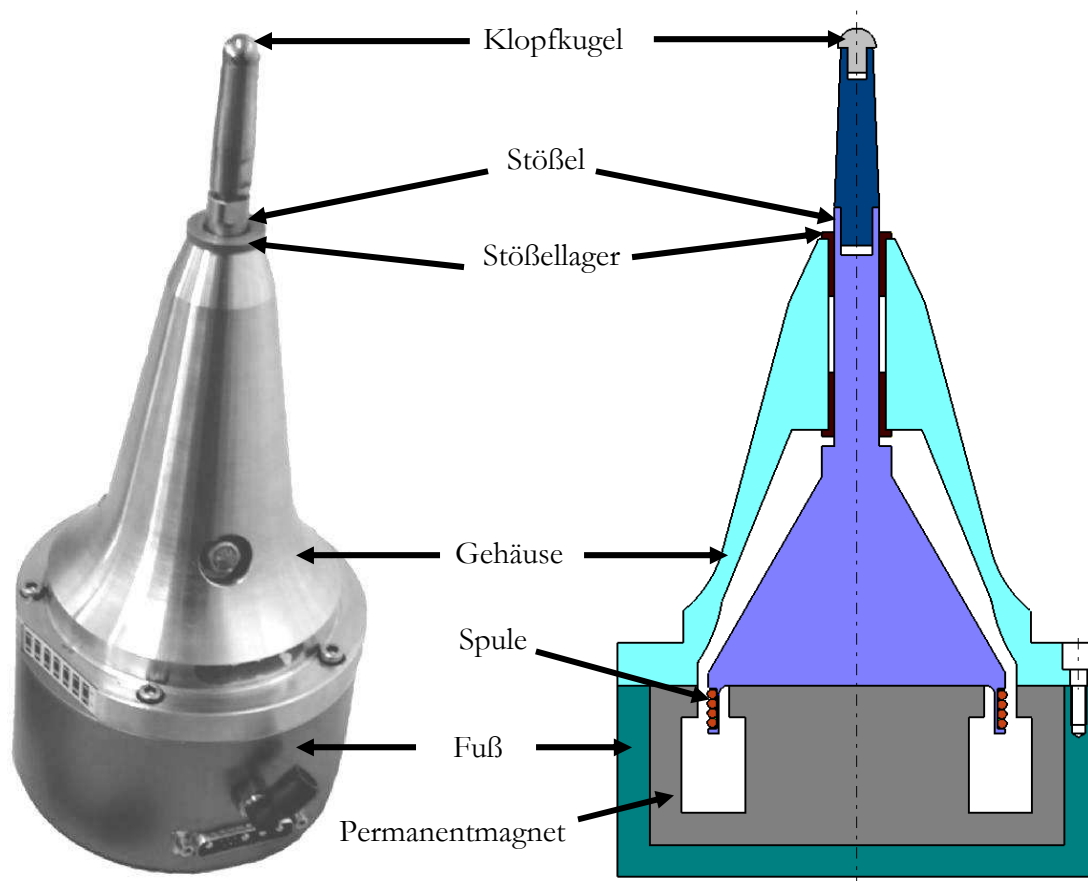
Elektrodynamisches Schlagwerkzeug der Fa. KWL
